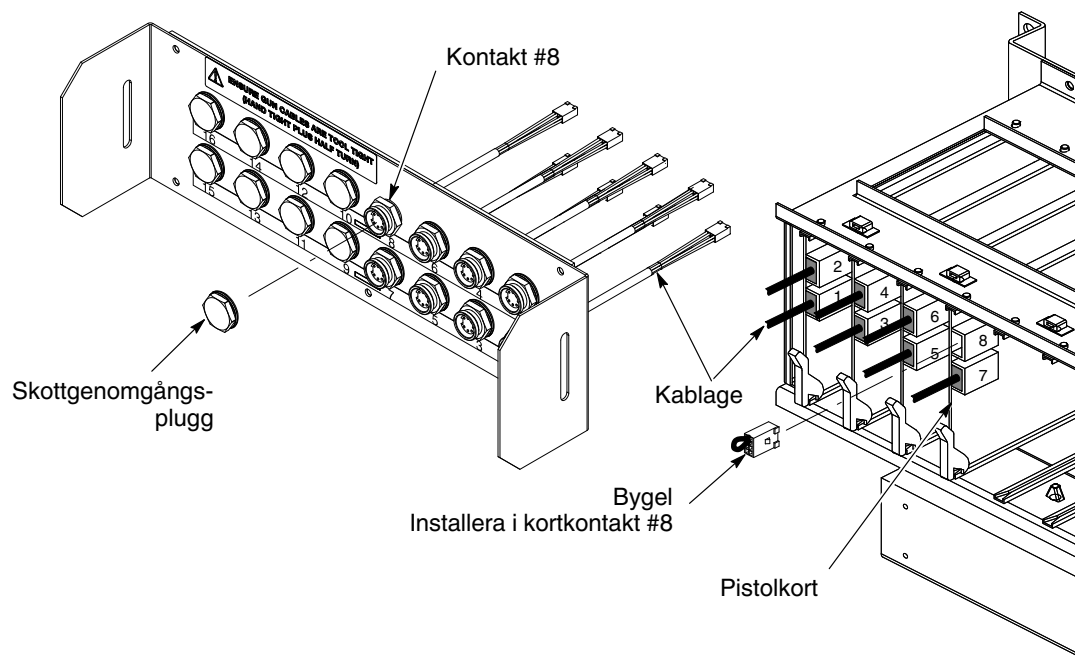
Installation av plugg och bygel - Exempel med 8 pistolers system med endast 7 pistoler
